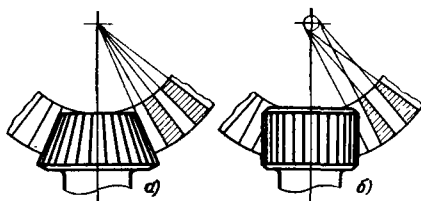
Схемы передач: a — конической; b — цилиндроконической
